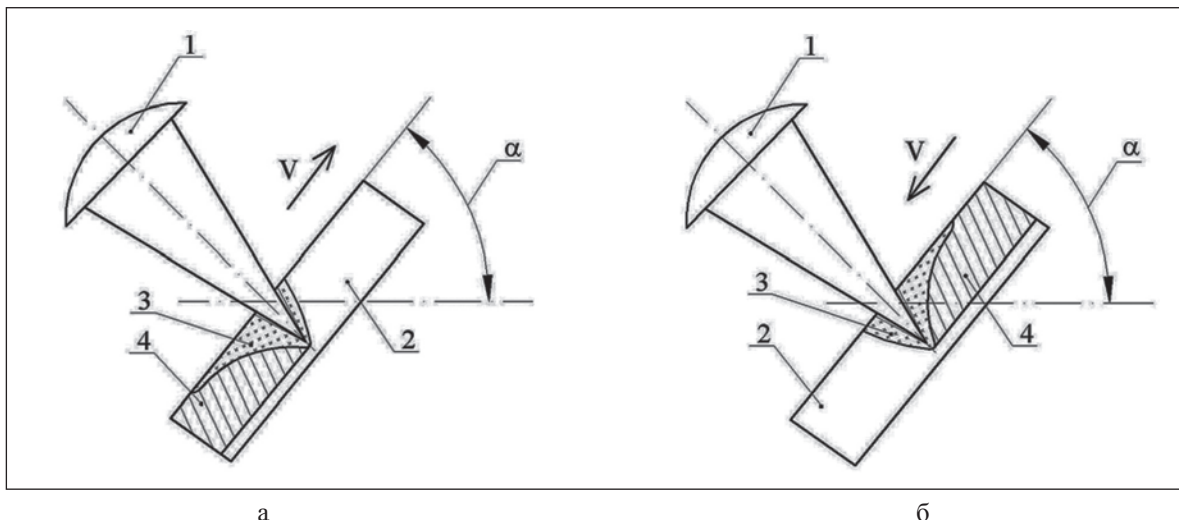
Схеми лазерного зварювання «на підйом» (а) та «на спуск» (б): 1 – пучок лазерного випромінювання, що фокусується лінзою; 2 – пластина; 3 – зварювальна ванна; 4 – метал шва; α – кут нахилу пластини до горизонтальної площини; V – напрям зварювання
